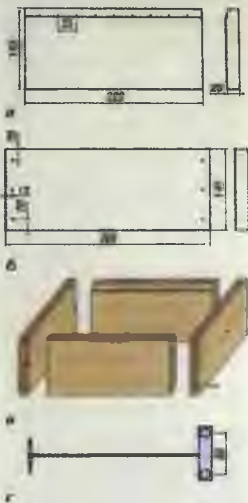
Корпус: а — торцевая стенка; б — боковая стенка; в — сборка корпуса; г — захват для переноски
